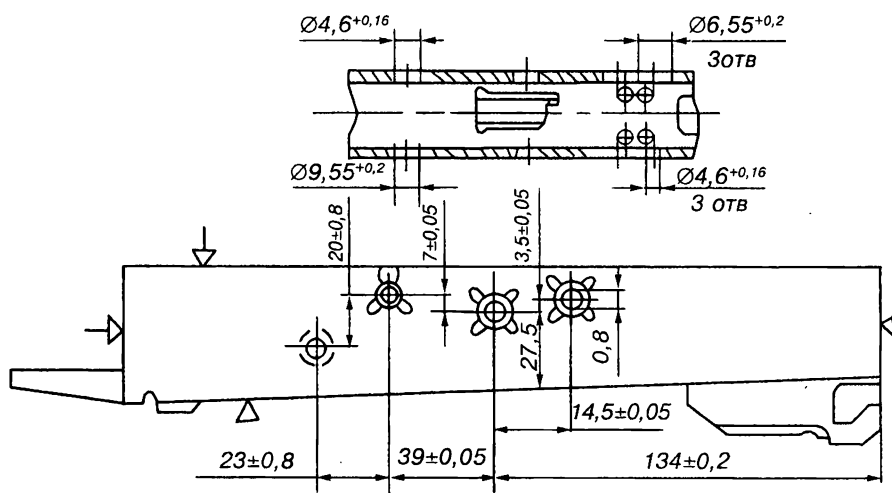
Сверление отверстий на агрегатно-сверлильном станке модель ХА153П
